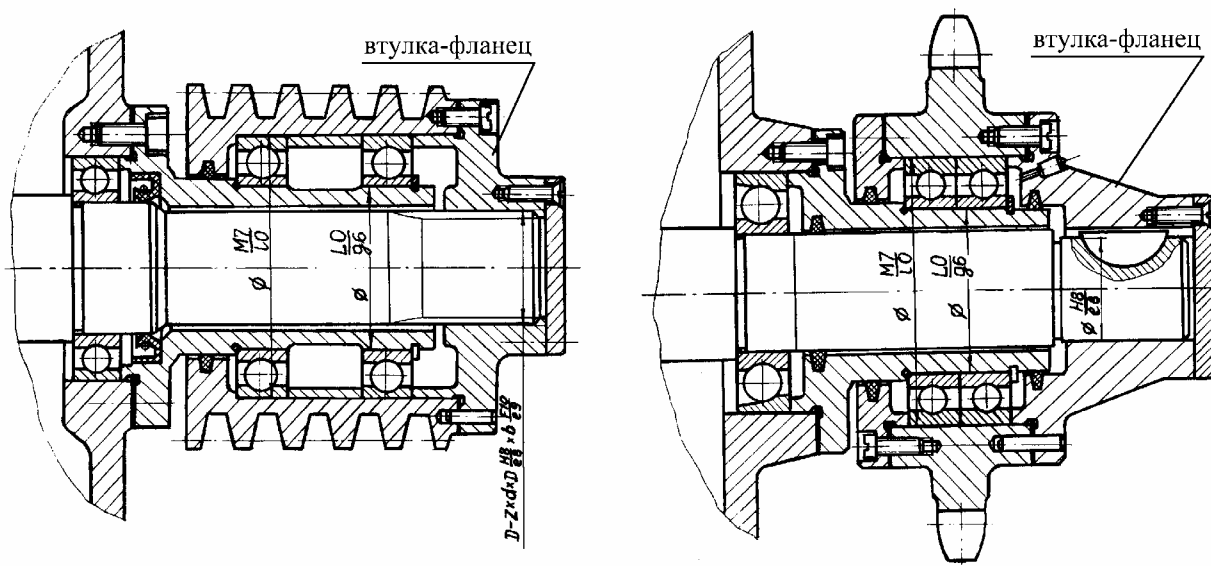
Установка шкива и звездочки с разгрузкой консольного конца вала от действия изгибающего момента
